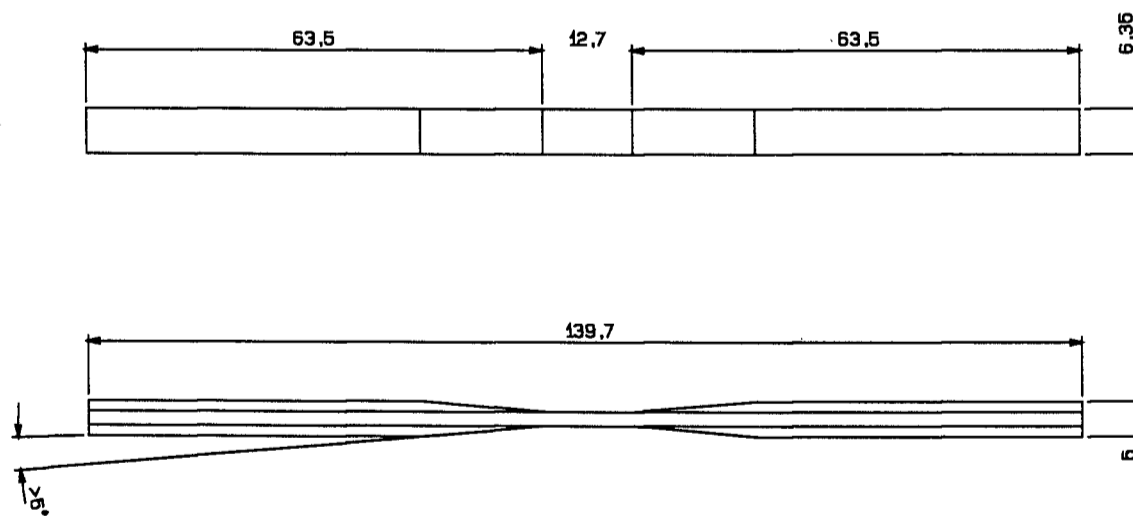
Geometria e dimensões do corpo-de-prova de compressão longitudinal e transversal.
